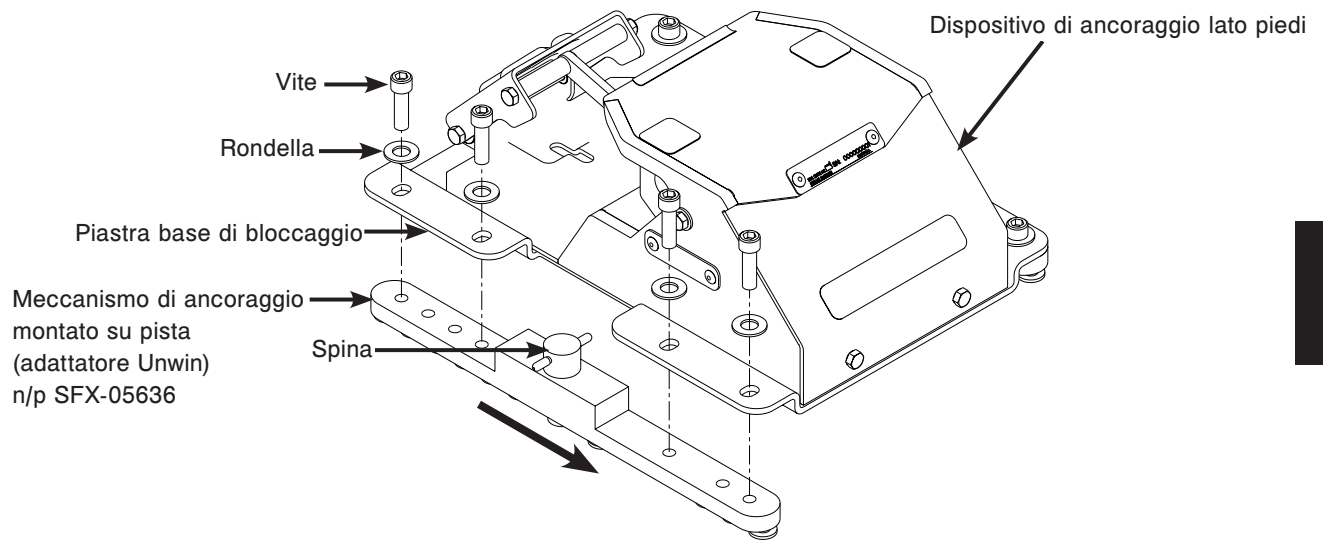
Assemblare il dispositivo di ancoraggio per lato piedi
